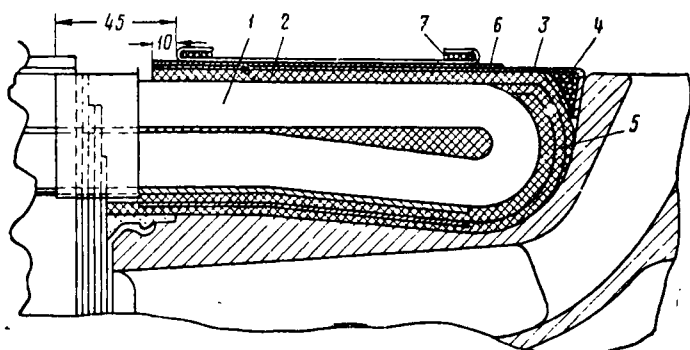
Разрез задней лобовой части неразрезной обмотки якоря тягового двигателя ДК-103А:
